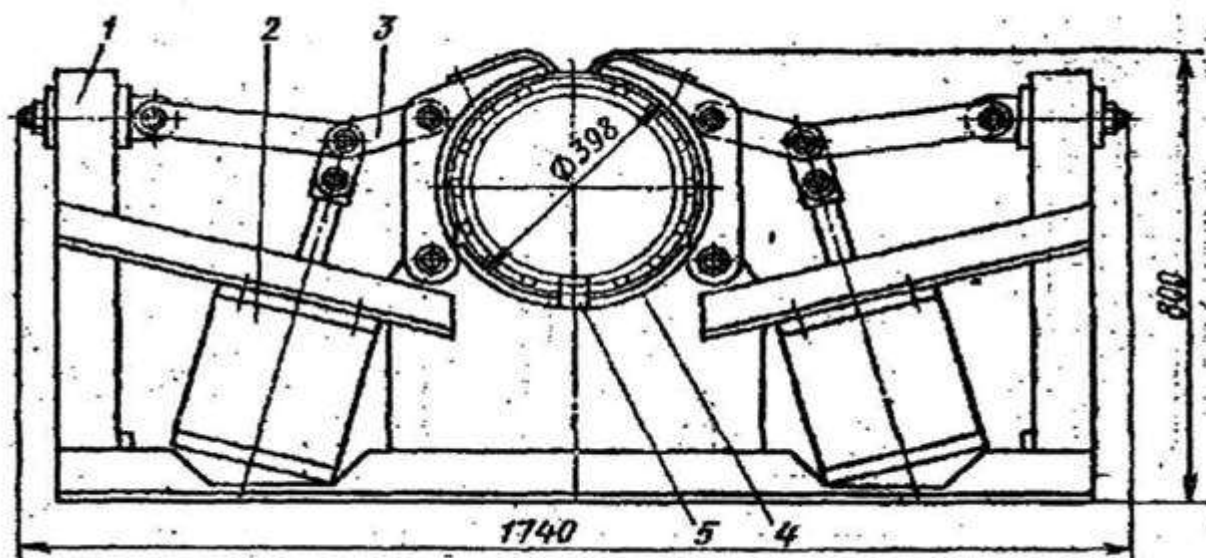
Приспособление для сборки продольных стыков обечаек малого диаметра
